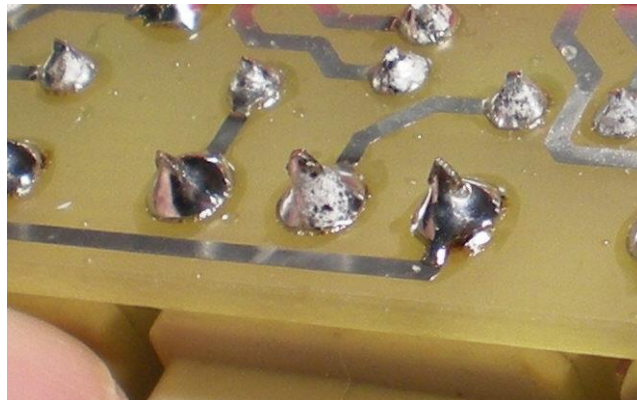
Exemples d'une soudure sèche encadrée par deux bonnes soldes au premier plan
